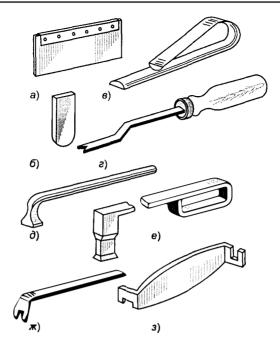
Набор инструмента обмотчика: a — фибровая пластинка; δ — фибровый язык; s — обратный клин; e — угловой нож; d — выколотка; e — топорик; m и g — ключи для гибки роторных стержней
